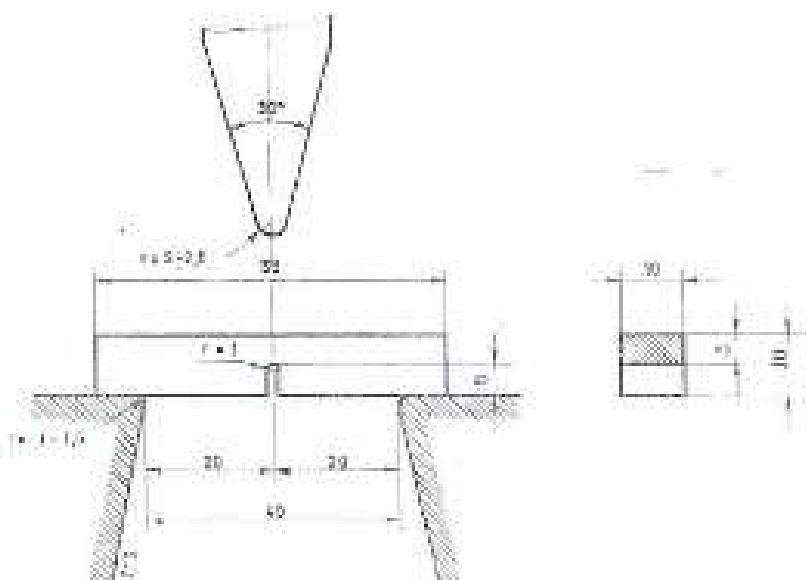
Parte parte del ensayo de impacto de Charpy
